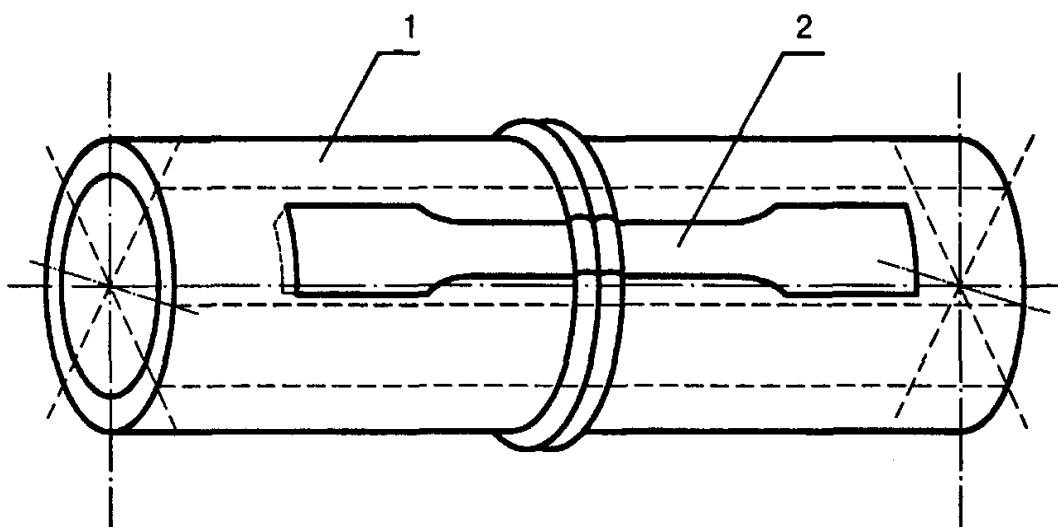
Схема вырезки образцов из сварного соединения для испытания на осевое растяжение
